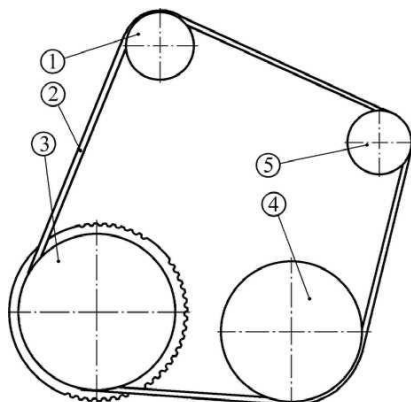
Схема установки ремня привода вспомогательных агрегатов:
